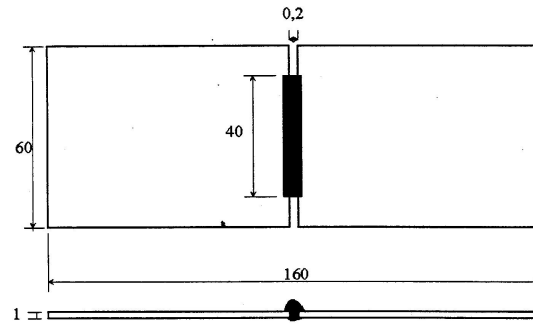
Corpo de prova soldado de topo, unidades em mm.
